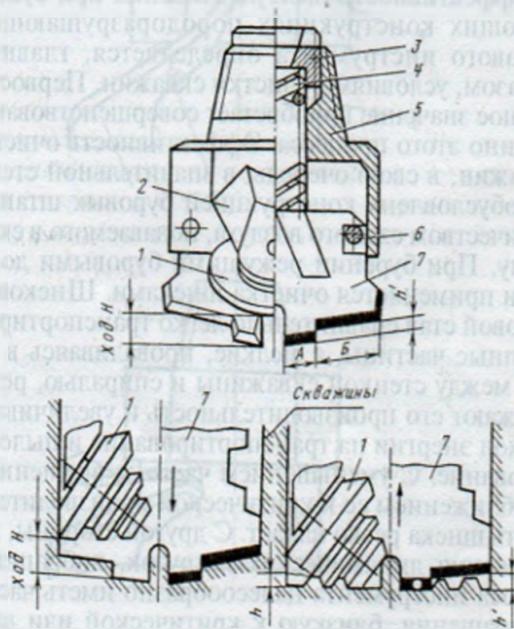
Режуще-шарошечное долото конструкции КузГТУ
